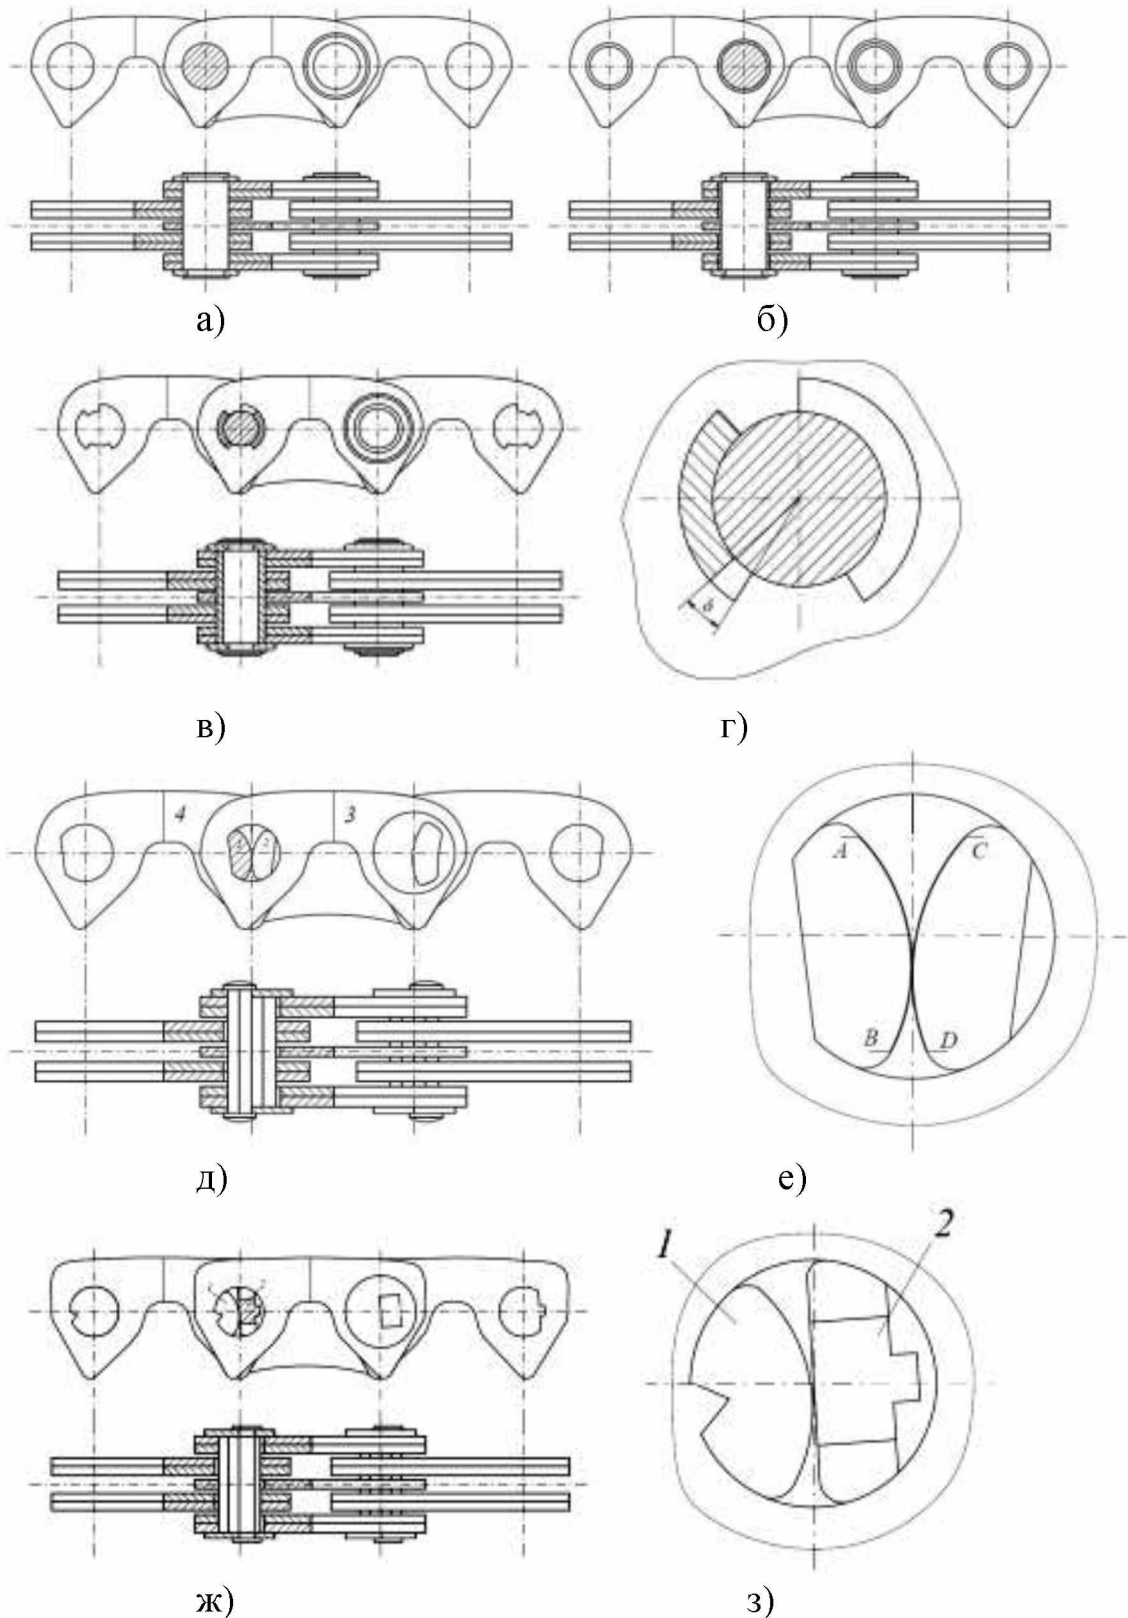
Види зубчастих ланцюгів: а – простий зубчастий ланцюг з валиком; б - простий зубчастий ланцюг з валиком і сталевією втулкою; в – зубчастий ланцюг із вкладишами; г - шарнір зубчастого ланцюга з вкладишами в
